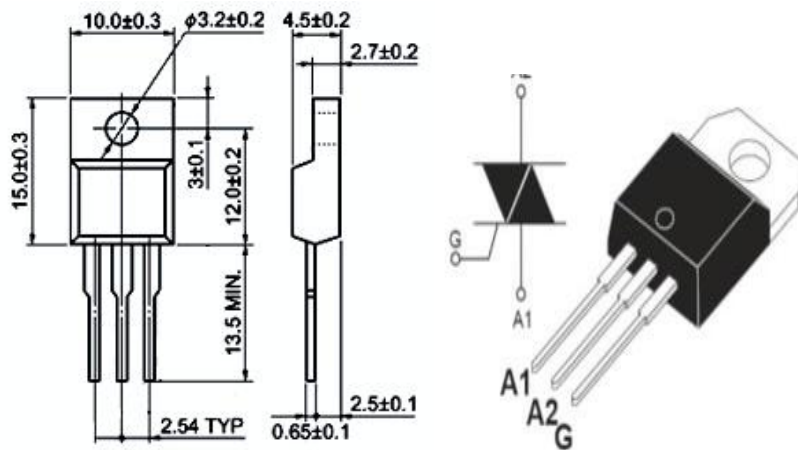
Габаритні розміри симистора типу BT136-600E
